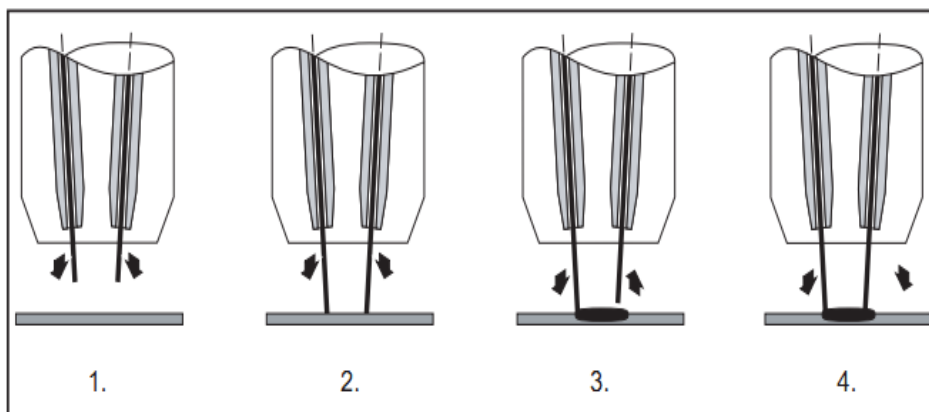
Úprava kovu pro vznik možného spojení [13]
